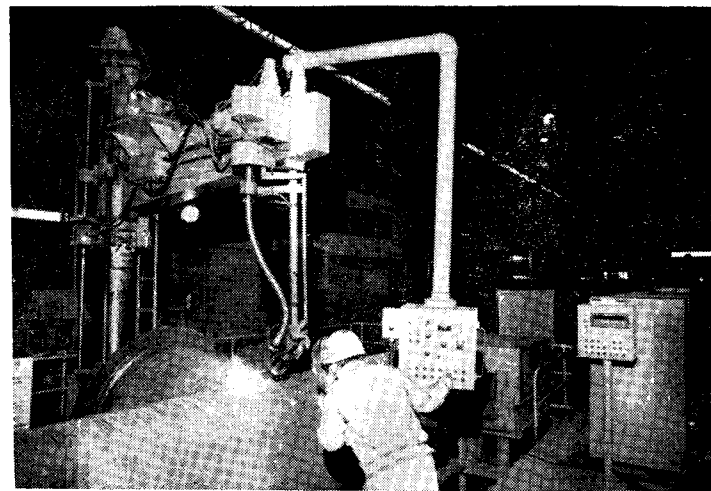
Автоматическая сварочная машина для сварки патрубков на трубах большого сечения.
